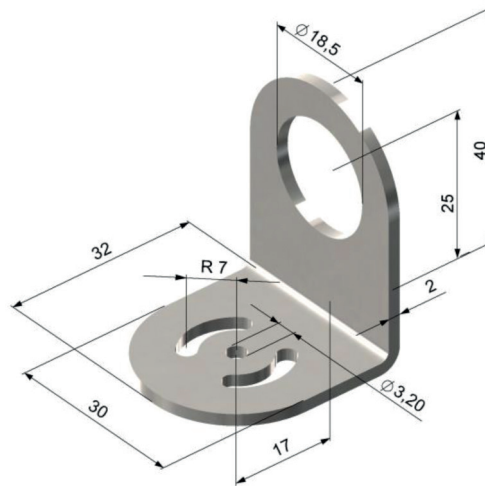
Montagewinkel, justierbar in einer Achse für HS [TM-FBMH-CT]
